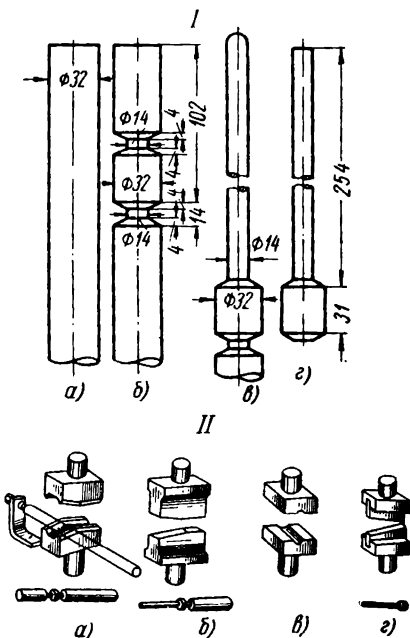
Пример штамповки на вертикально-ковочной машине: I — переходы штамповки; II — бойки для них; I-a — заготовка; I-b — заготовка обработана в ручье II-a; I-в — конец протяннут в ручье II-b и отделан в ручье II-в; I-г — готовая поковка (конец обрезан и отделан от прутка в ручье II-г)
